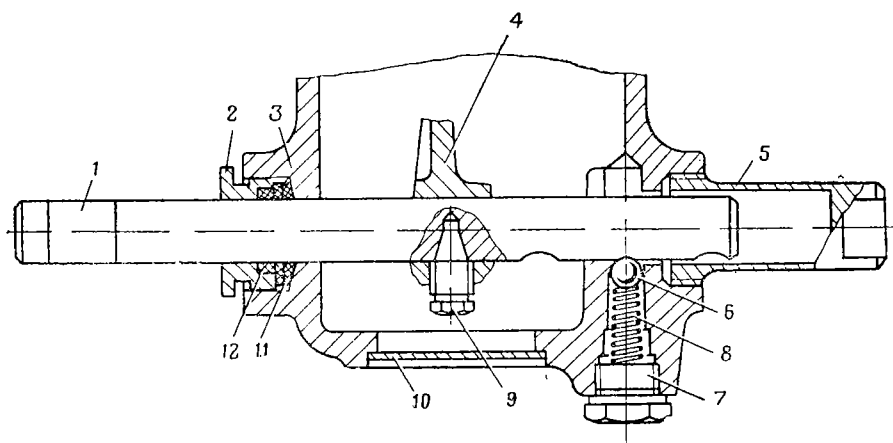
Фиксаторный механизм коробки отбора мощности привода водометного движителя:
